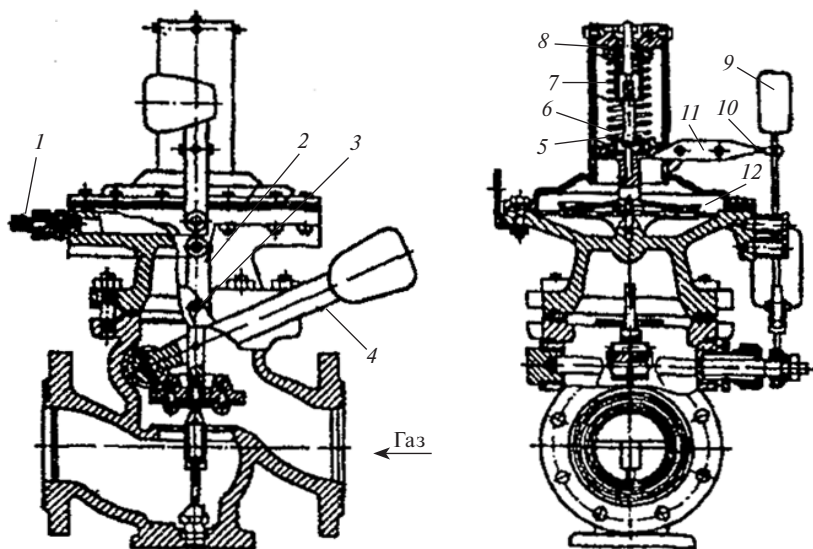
Предохранительно-запорный клапан ПКН (ПКВ):
